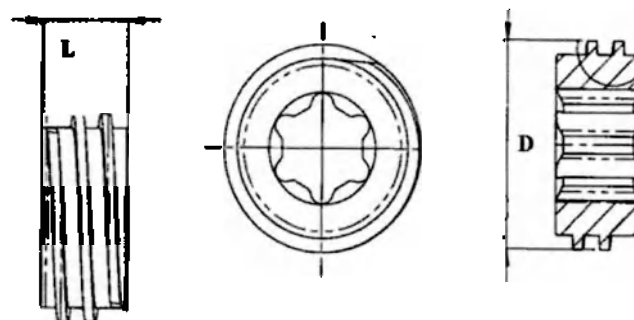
Винт блокирующий MUST MINI (1 шт./уп.);
